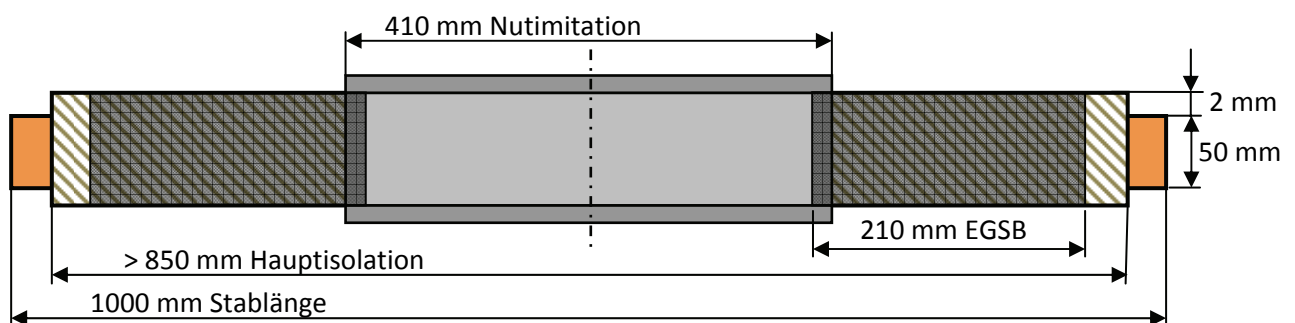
VPI Stab mit aufgeschweißter Nutimitation
